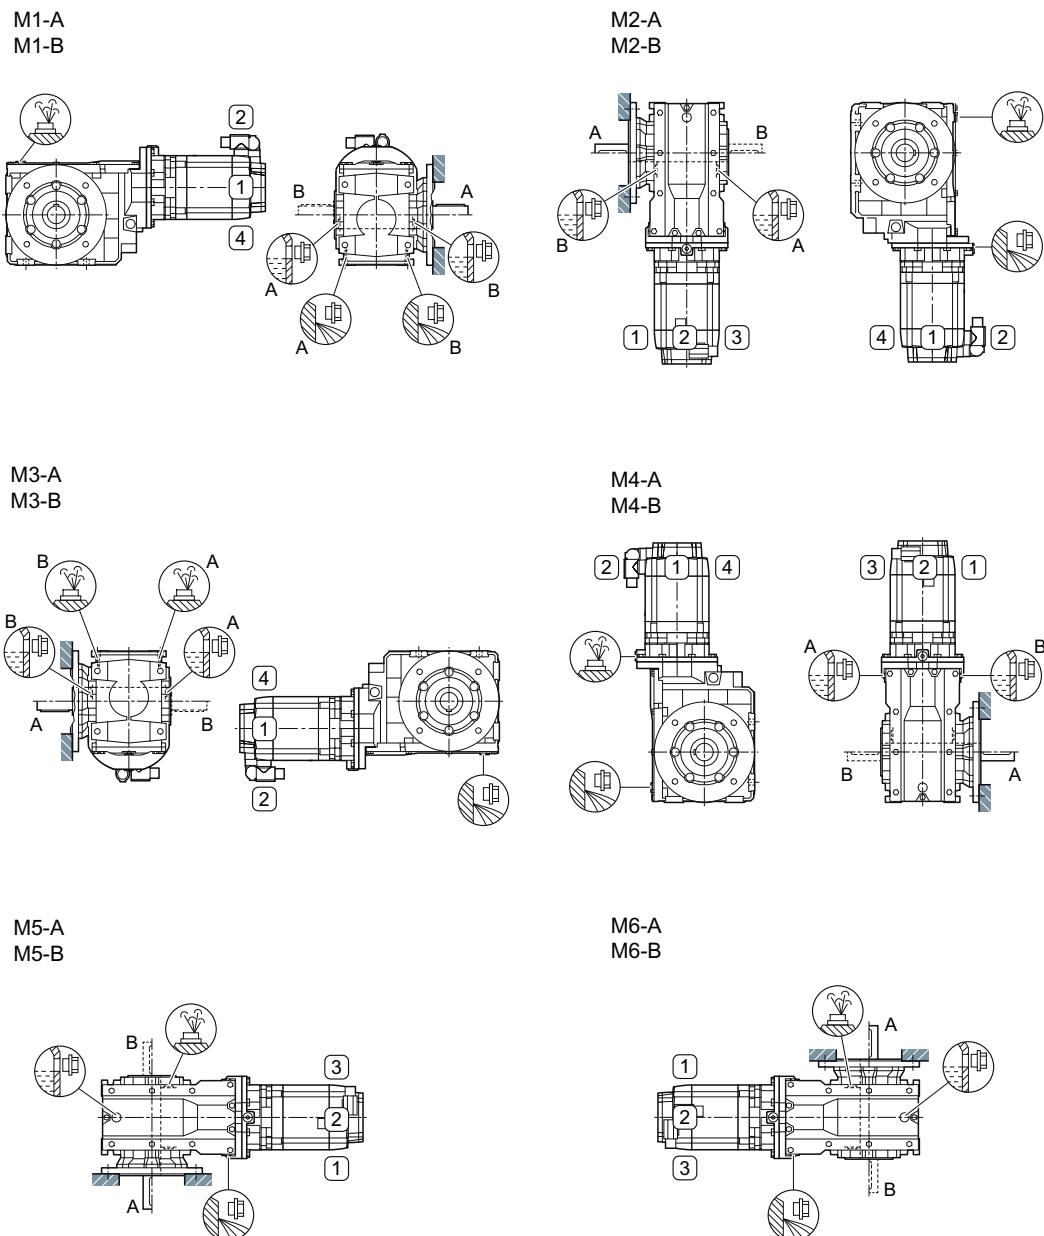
Einbaulagen für Servo-Kegelradgetriebemotor B.F (Flanschausführung) oder B.Z (Gehäuseflanschausführung), Baugrößen 39 - 49, 2-stufig
